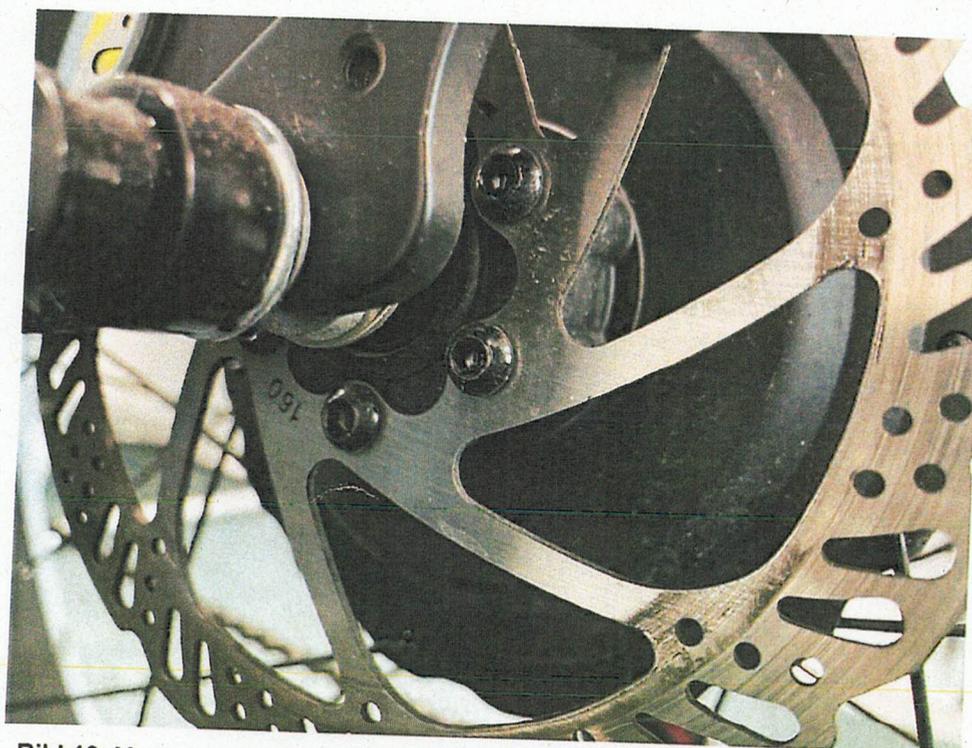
Verschraubung Bremsscheibe hinten mangelhaft / gelockert
